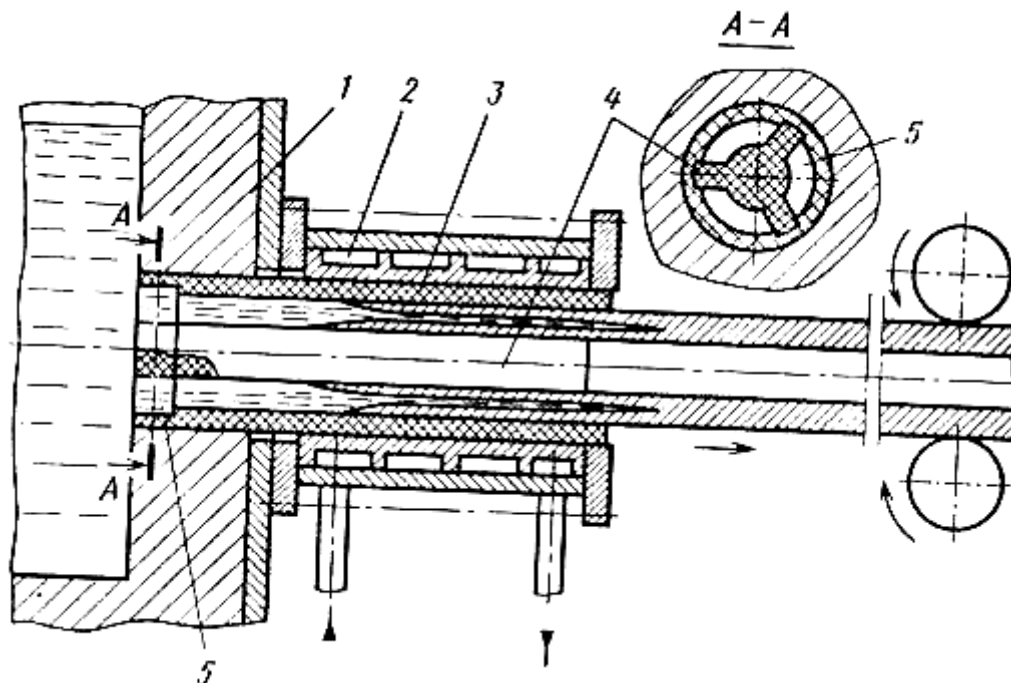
Схема кристаллизатора для горизонтального непрерывного литья трубчатых заготовок и профилей 1-раздаточная печь; 2-водоохлаждаемая рубашка; 3-графитовый вкладыш; 4-стержень; 5- отверстия для подвода расплава
